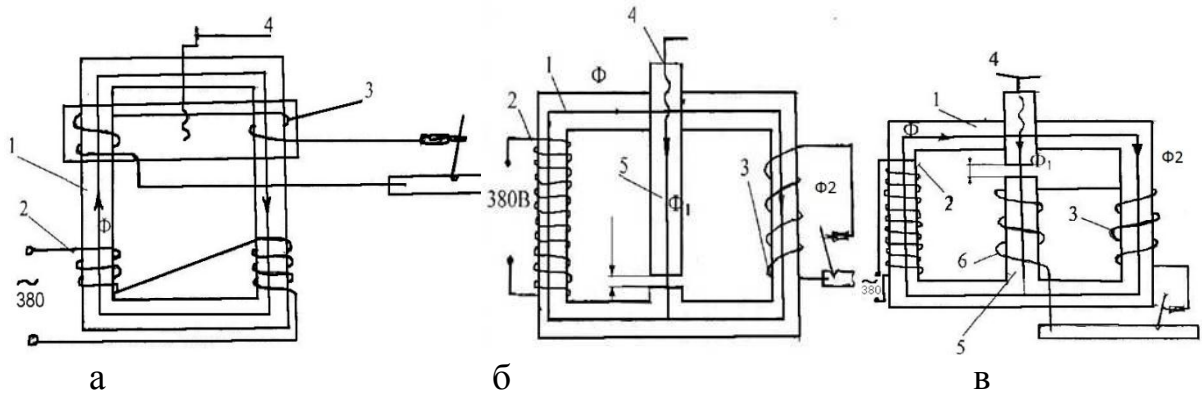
Принципиальные схемы однофазовых сварочных трансформаторов:
